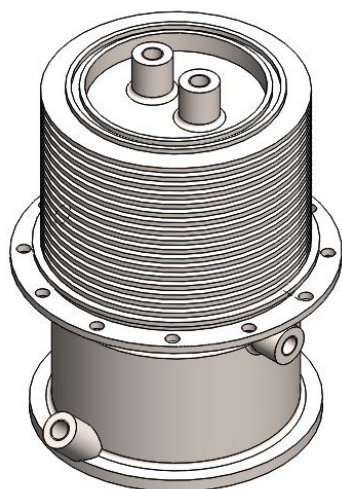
vue de l'échangeur de tête de la machine réalisée en prototypage 3D.
